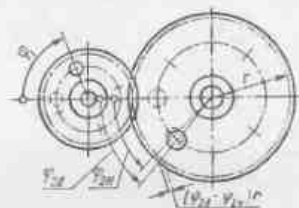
Схема к определению кинематической погрешности зубчатой передачи
